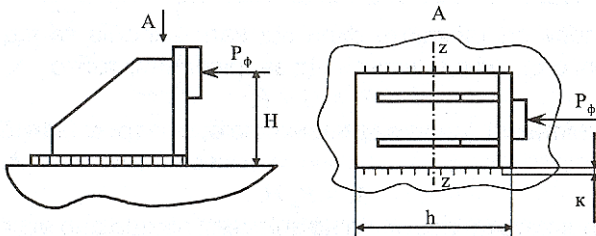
Розрахункова схема закріплення упора зварними швами [2]
